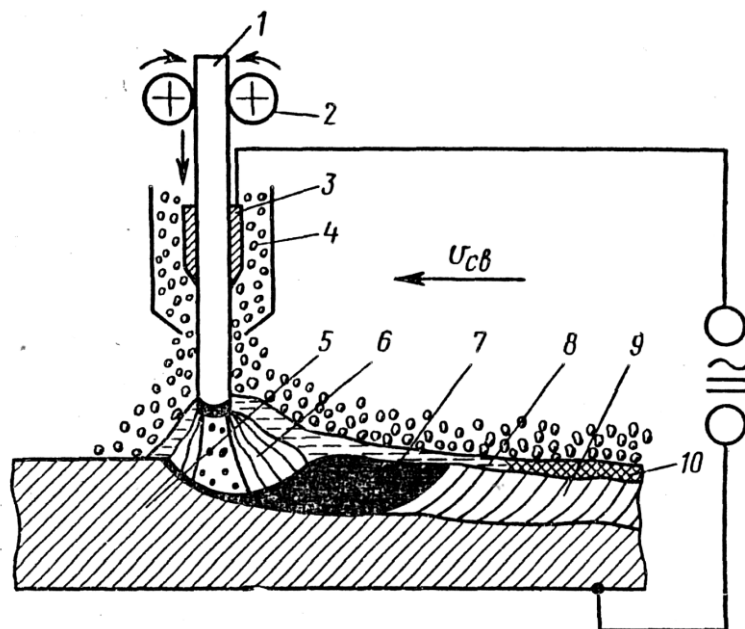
Схема автоматической сварки под флюсом:
